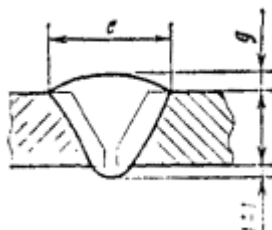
Конструктивные элементы шва сварного соединения
